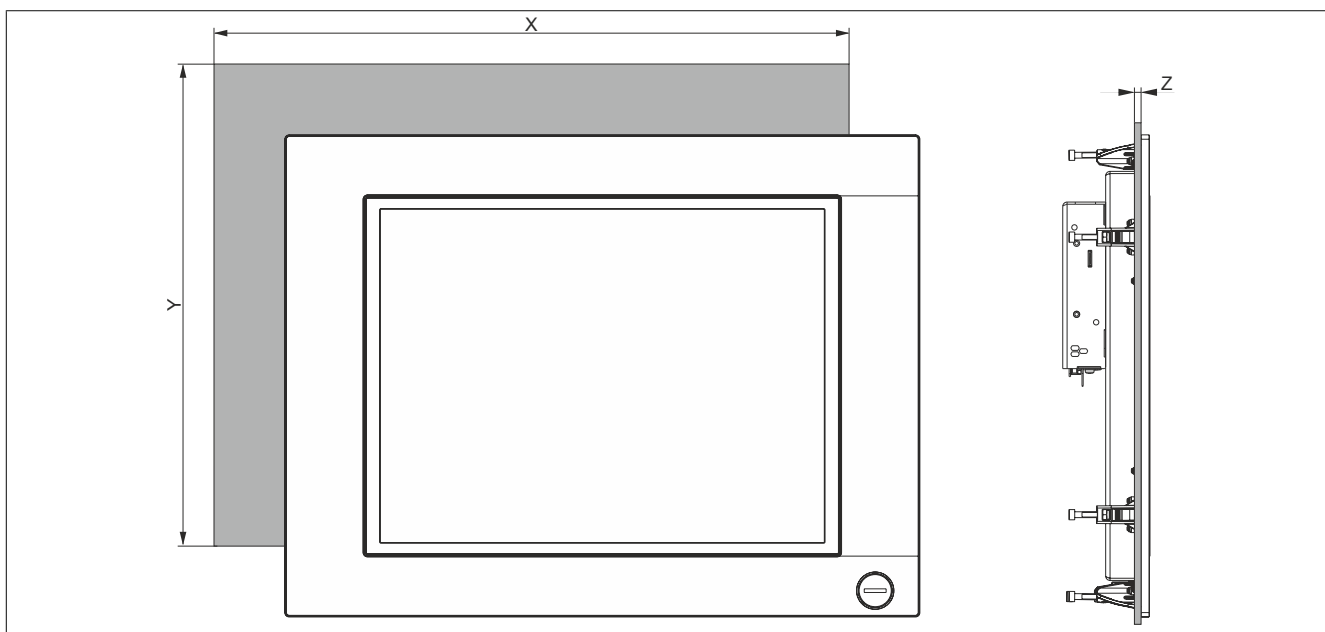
Устройство Panel PC 2200 на базе панелей AP1000 с зажимными блоками — монтажный чертеж
